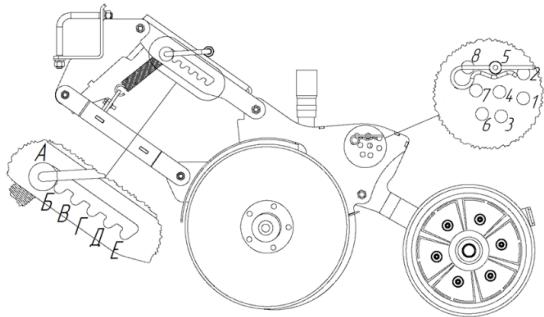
Регулировочные параметры копирующего двухдискового сошника;
